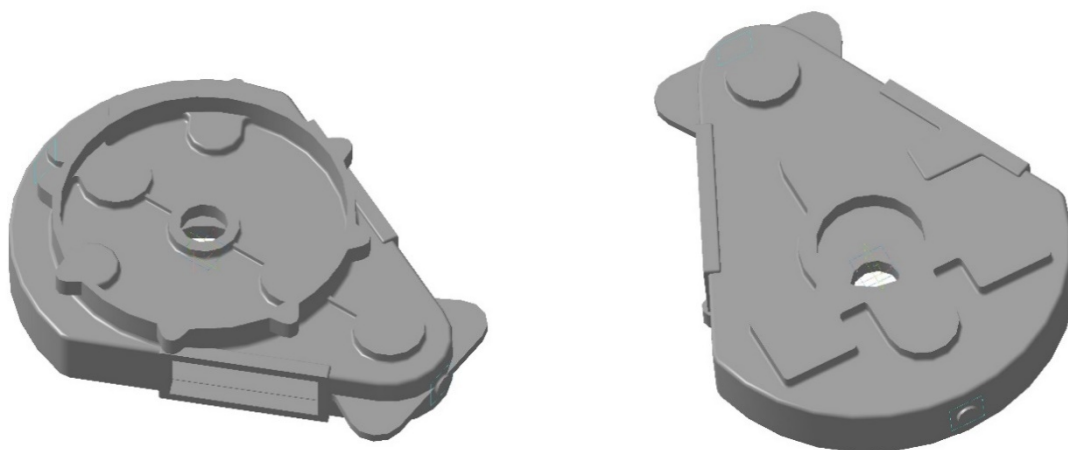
3D-модель заготовки детали "Корпус цилиндрического редуктора"
